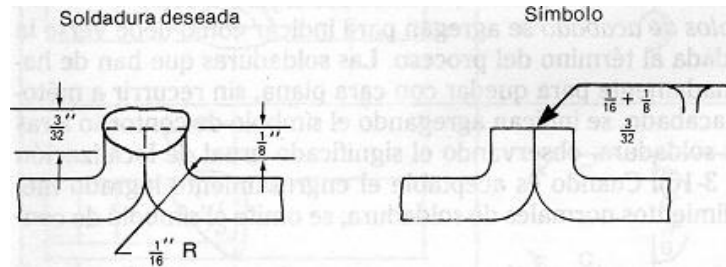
Símbolo de la soldadura en el que se especifica una soldadura de brida con radio y altura de la soldadura sobre el unto de tangencia.
